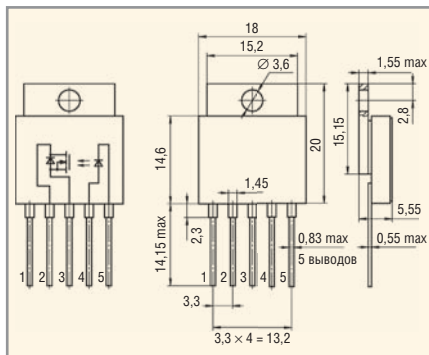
Чертёж корпуса и электрическая схема реле 5П163
